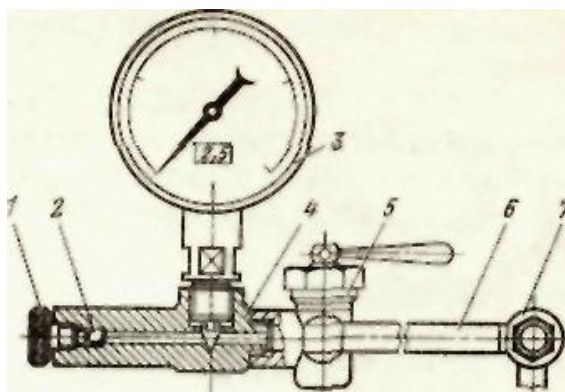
Пристосування для перевірки тиску палива: 1 - гвинт прокачування; 2 - клапан; 3 - манометр; 4 - корпус; 5 - трьохходовий кран; 6 - шланг; 7 - перехідний штуцер
